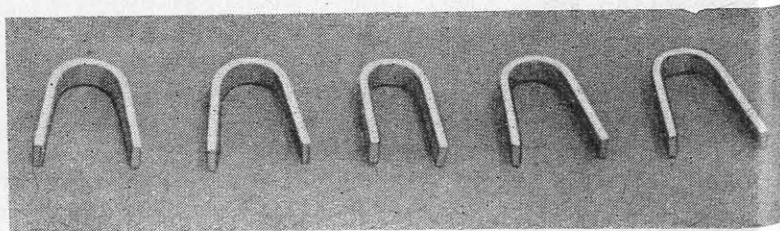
Образцы на загиб, сваренные автоматической сваркой.
